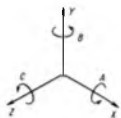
Расположение осей координат и обозначение движений инструмента в станках с ЧПУ
